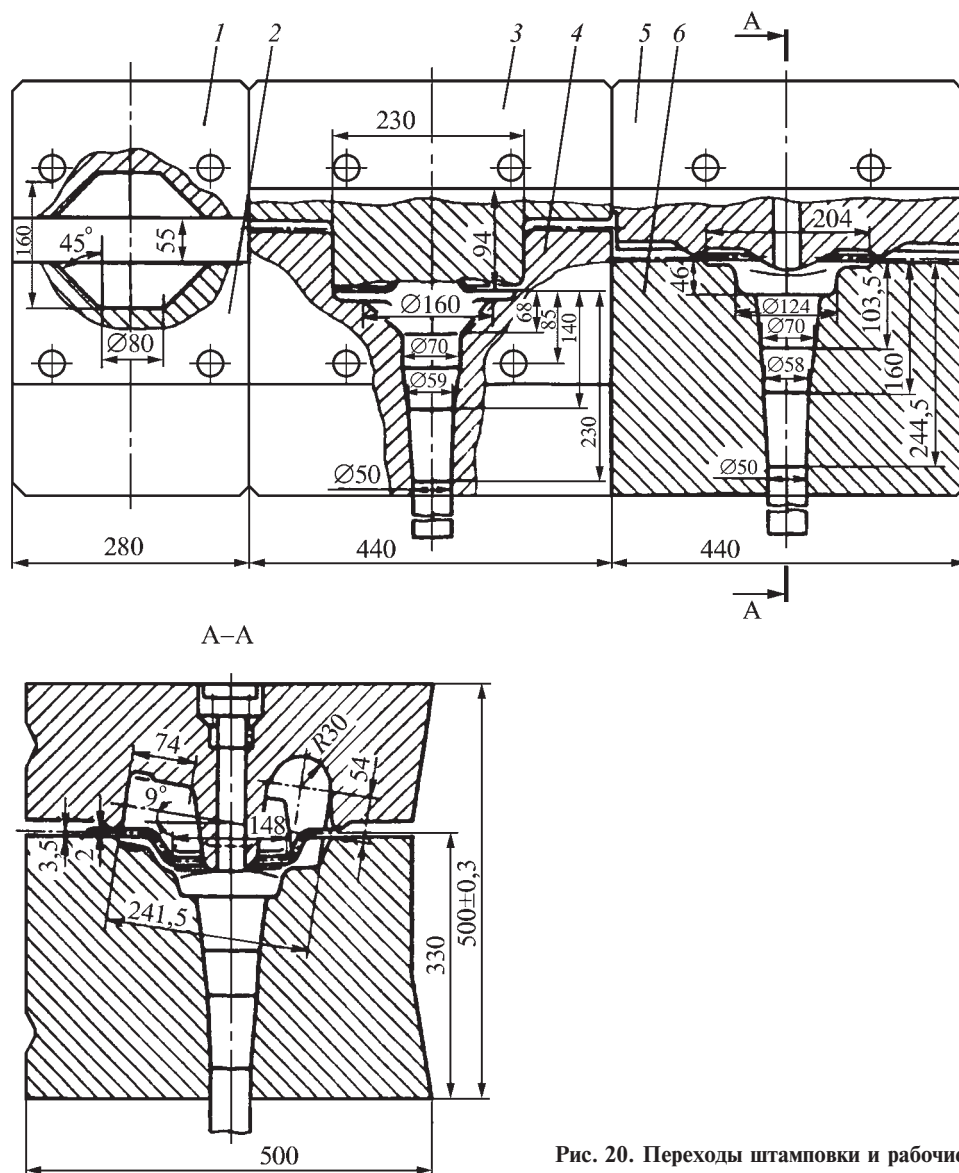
Переходы штамповки и рабочие вставки для поковки поворотного кулачка
